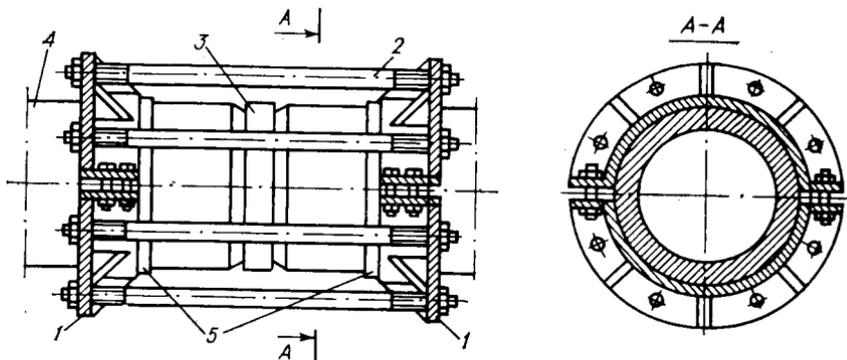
Стяжное приспособление для холодного натяга трубопровода:
